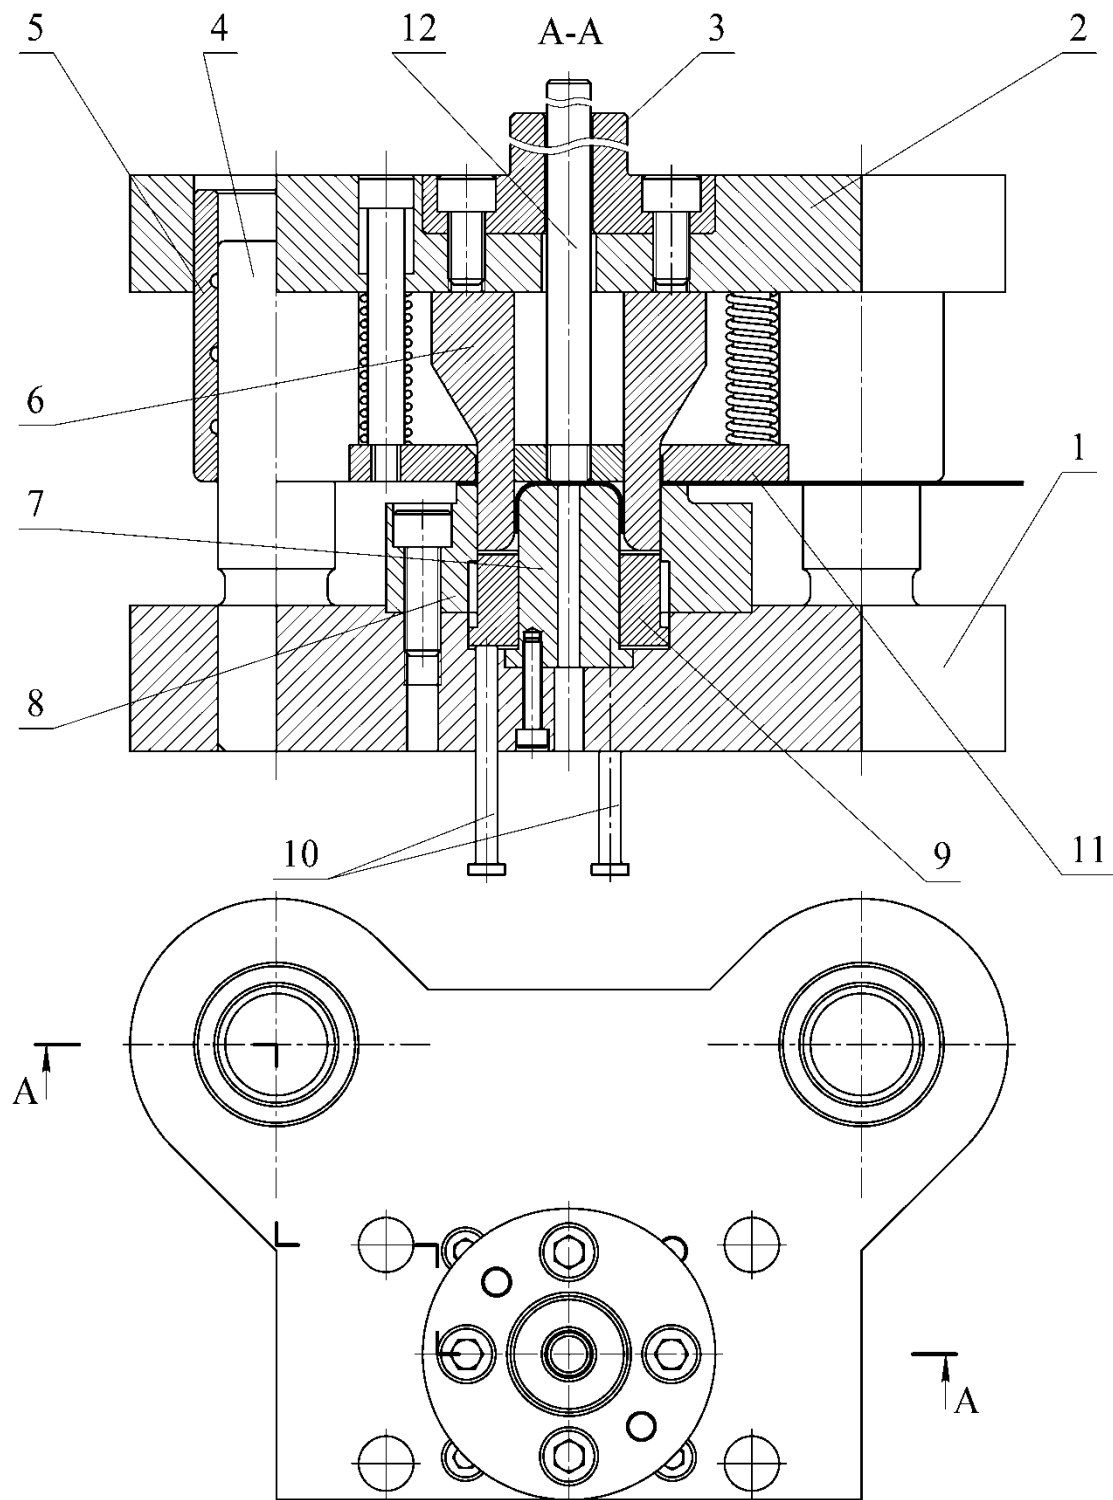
Схема комбинированного штампа для изготовления детали методом формовки-вытяжки: 1 – плита нижняя, 2 – плита верхняя, 3 – хвостовик, 4 – направляющая колонка, 5 – направляющая втулка, 6 – матрица вытяжная – пуансон вырубной, 7 – вытяжной пуансон, 8 – матрица вырубная, 9, 10 – нижний выталкиватель, 11 – прижим, 12 – верхний выталкиватель
